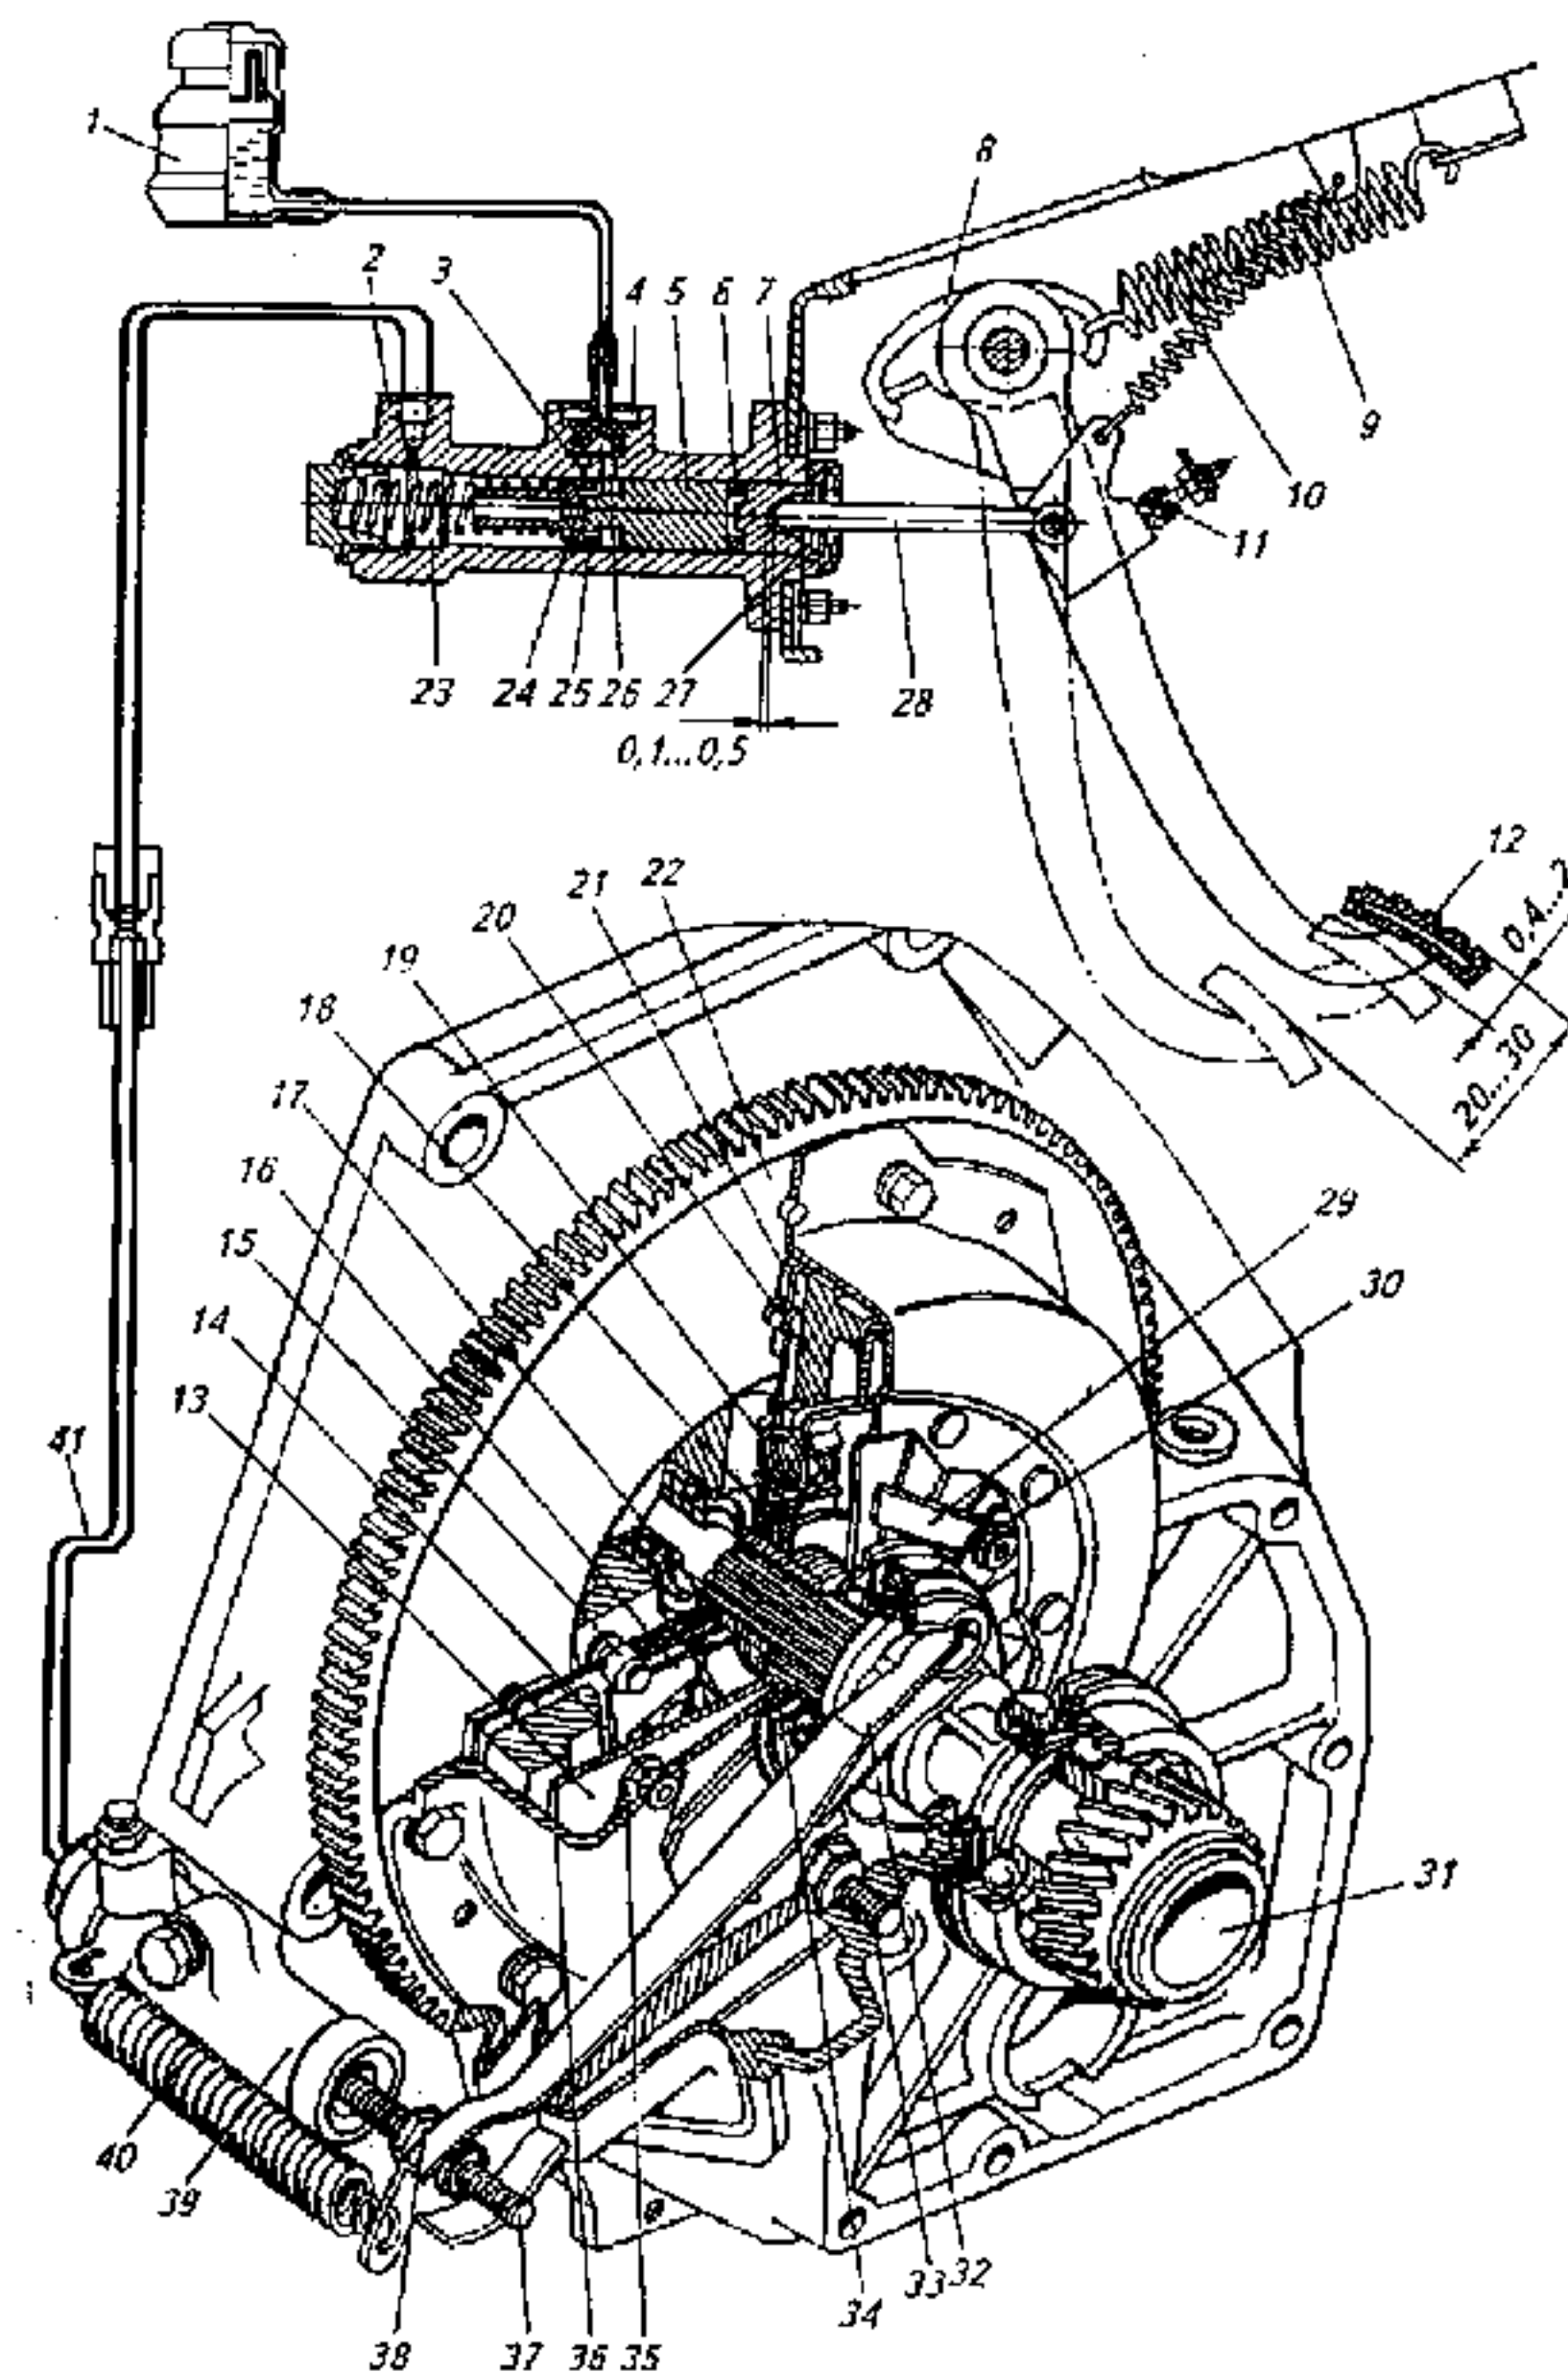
Сцепление и привод сцепления автомобиля ВАЗ-21213: 1 — бачок для тормозной жидкости; 2 — главный гидроцилиндр; 3 — компенсационное отверстие; 4 — штуцер; 5, 7 — поршни; 6, 25 — уплотняющие манжеты; 8 — крючок; 9 — пружина сервопривода; 10, 40 — оттяжные пружины; 11 — винт (ограничитель хода педали); 12 — педаль; 13 — диафрагменная нажимная пружина; 14 — опорная заклепка; 15 — ступенчатая заклепка; 16 — наружная пластина ведомого диска; 17 — ступица ведомого диска; 18 — фланец ступицы; 19 — демпферная пружина; 20 — нажимной диск; 21 — ведомый диск; 22 — маховик; 23 — пружина; 24 — перепускное отверстие; 26 — впускное отверстие; 27 — стопорное кольцо; 28, 37 — толкатели; 29 — планка; 30 — выжимной подшипник; 31 — вал сцепления; 32 — вилка выключения сцепления; 33 — шаровая опора; 34 — упорный фланец; 35 — опорное кольцо диафрагменной пружины; 36 — кожух; 38 — регулировочная гайка; 39 — рабочий гидроцилиндр; 41 — трубопровод
